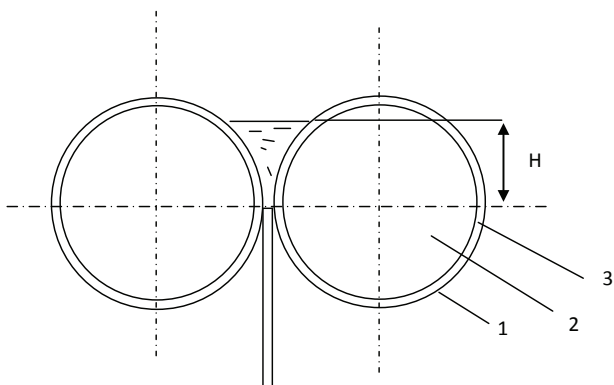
Схема формирования полосы на двухвалковой МНЛЗ: 1 – наружная медная стенка; 2 – стальная обечайка; 3 – щелевой зазор для прокачивания воды; Н – высота налива металла
